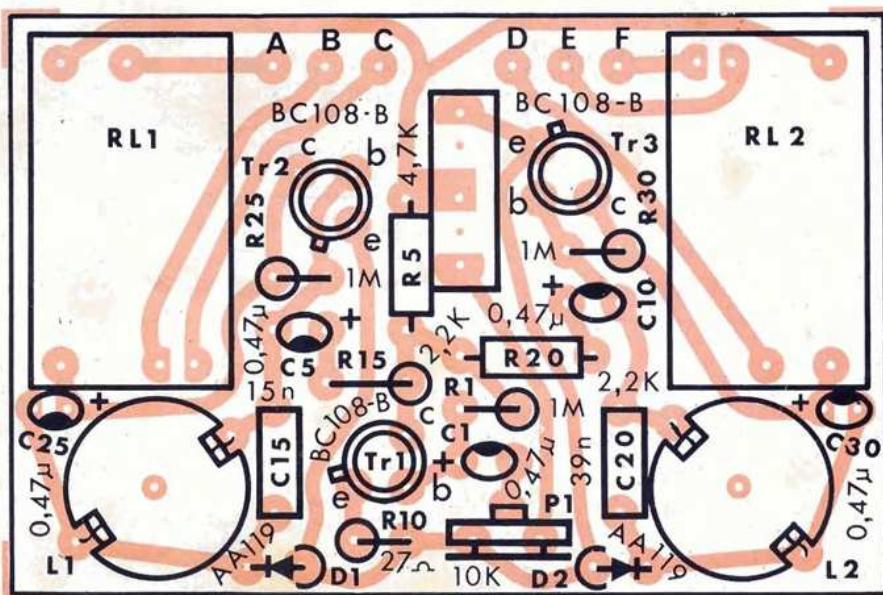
Montaggio dei componenti sulla bassetta a circuito stampato - UK 330/A.
